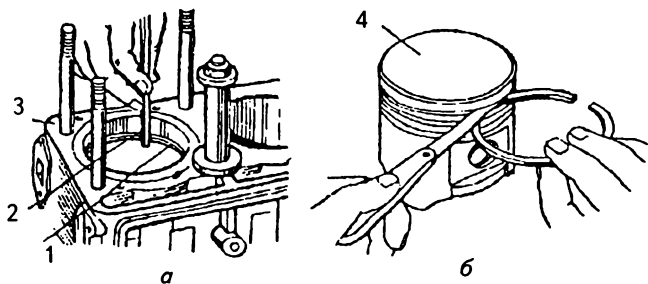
Проверка зазора в замке поршневого кольца (а) и бокового зазора между поршневым кольцом и канавкой в поршне (б): 1 — поршневое кольцо; 2 — щуп; 3 — блок цилиндров двигателя; 4 — поршень
